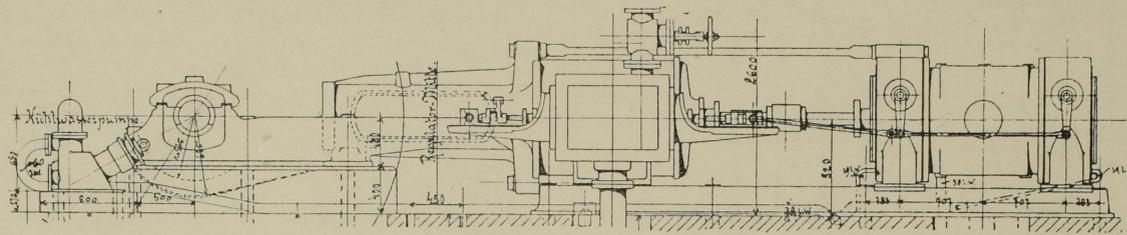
Seitenansicht der Maschine. Massst. 1:100.
